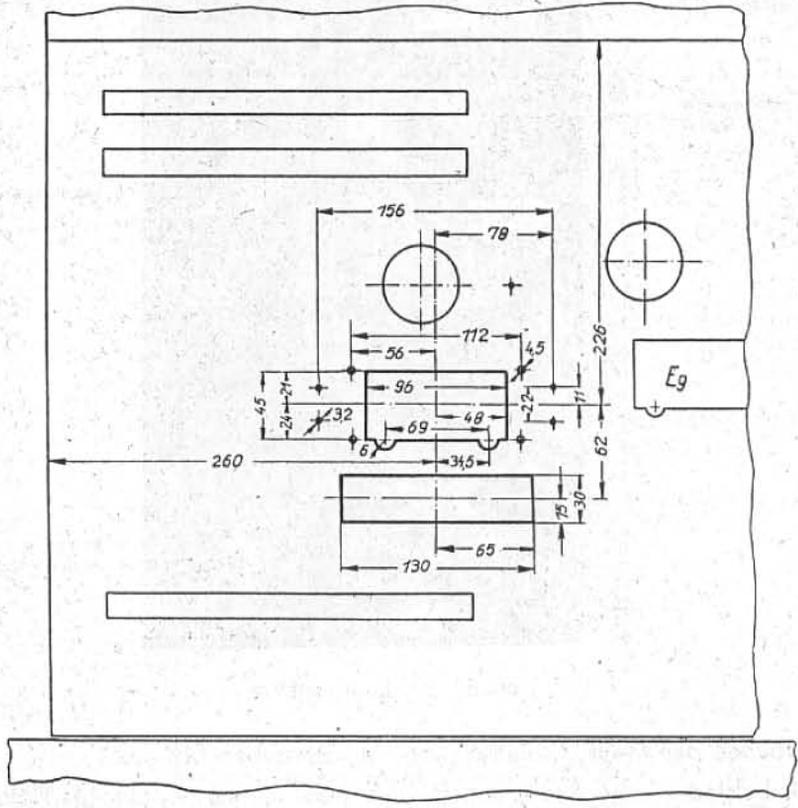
Maßskizze für den Durchbruch der Tj-Platte.
